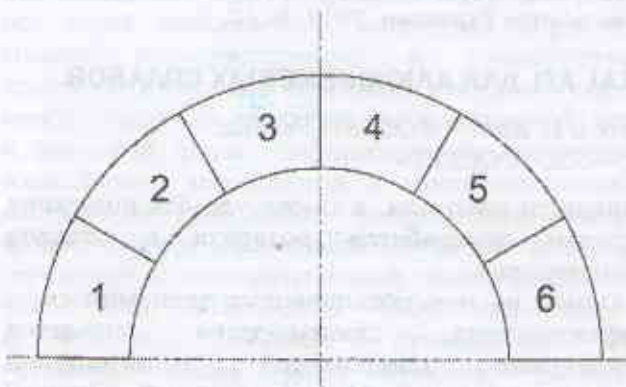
Схема окрашивания стержней и их расположения в форме для изготовления отливки «Обойма» массой 4,1 т
